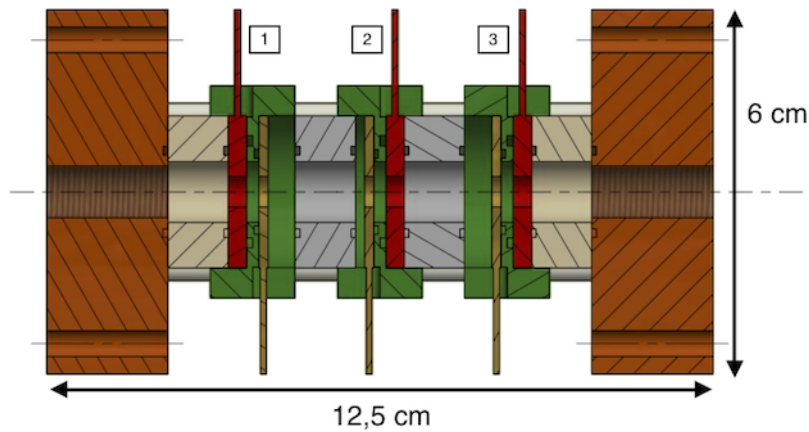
Vue en coupe du prototype de pompe LAPLACE3.
